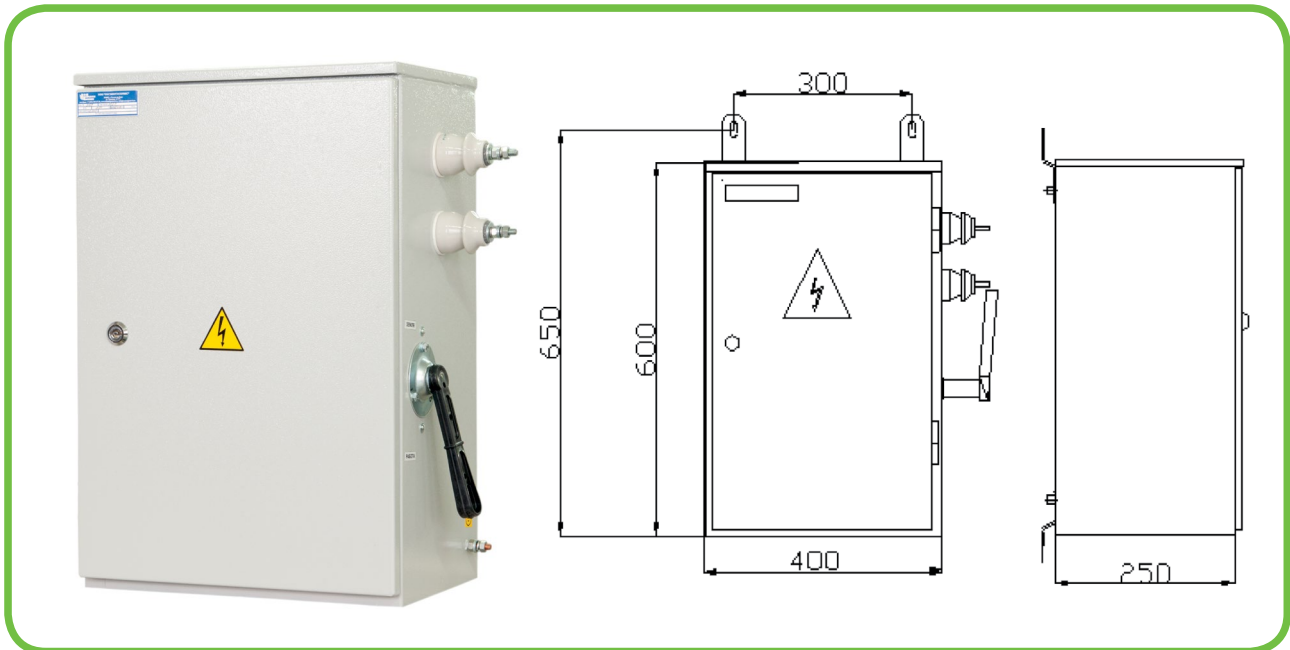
Общий вид и габаритные размеры шкафа отбора напряжения ШОН
